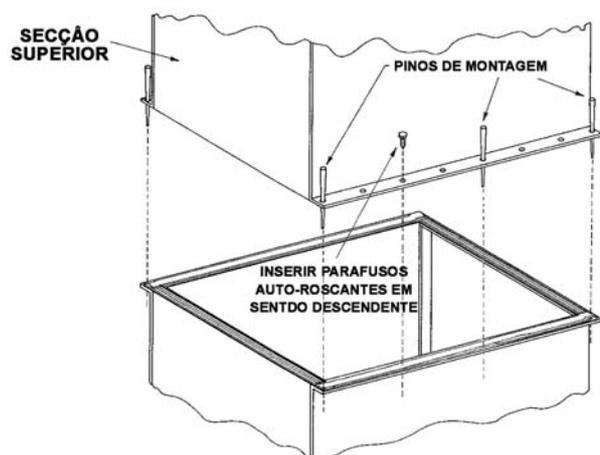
Montagem da secção de bateria / enchimento sobre a secção bacia / ventilador.
